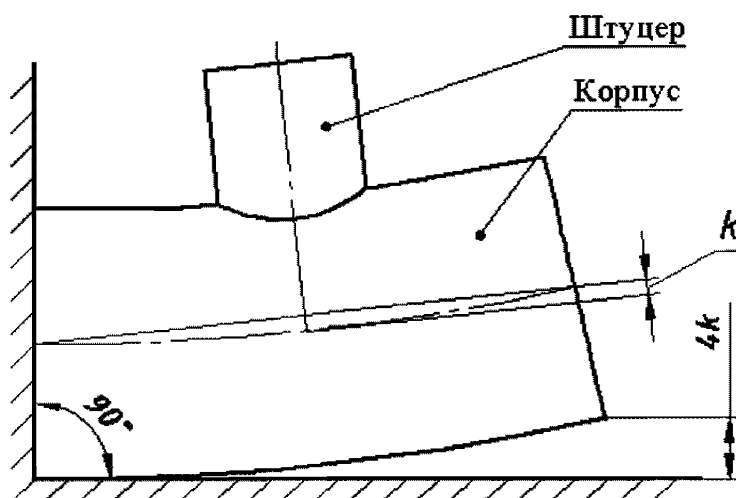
Отклонение от прямолинейности оси корпуса сварного тройника
